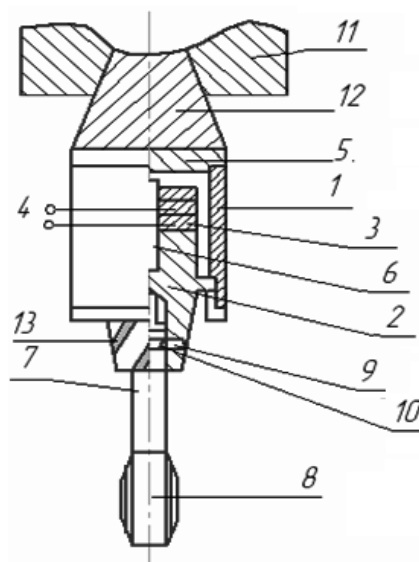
Ультразвуковой инструмент для нарезания резьбы
